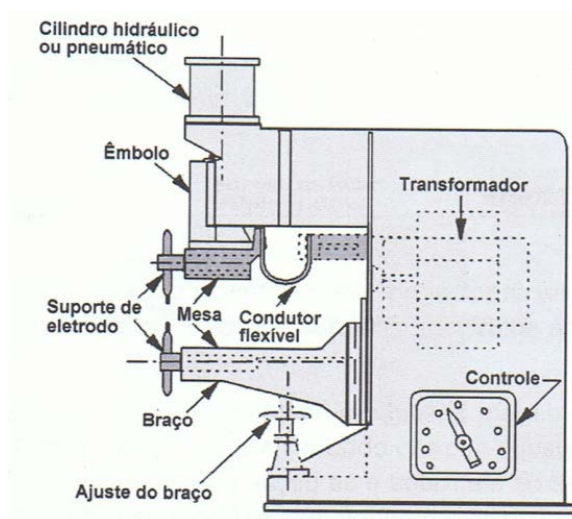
Equipamento de soldadura por resistência por pontos [1]
